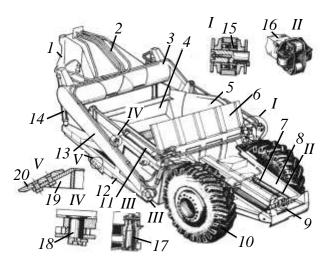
Оборудование скрепера МоАЗ-6014: 1 — стойка; 2 — хобот; 3 — поперечная балка тяговой рамы; 4 — заслонка; 5, 6 — боковая и задняя стенки ковша; 7 — гидроцилиндр задней стенки; 8 — буфер; 9 — балка; 10 — колесо; 11 — гидроцилиндр заслонки; 12 — днище ковша; 13 — упряжная тяга; 14 — гидроцилиндр ковша; 15 — направляющий ролик; 16 — толкатель; 17 — палец крепления тяговой рамы; 18 — палец крепления заслонки; 19 — подножевая плита; 20 — нож; 1, II, III, IV, V — разрез направляющего ролика, толкателя, крепления тяговой рамы, заслонки и ножей
